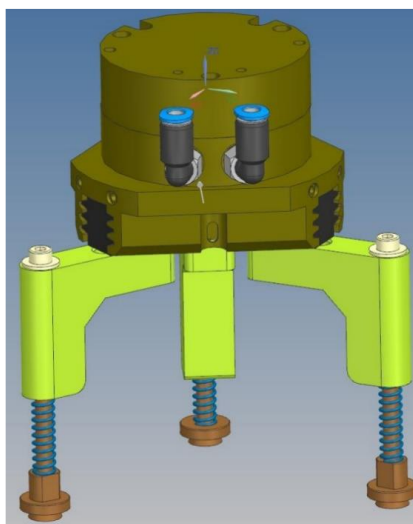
3D CAD-модель лівого захвату з пружинними пальцями
